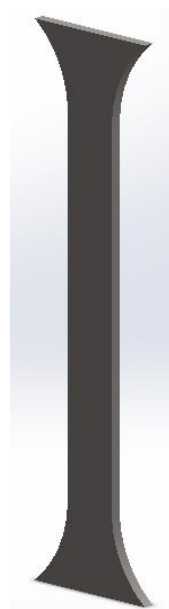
Géométrie 3D de l'éprouvette de traction sous Solidworks
